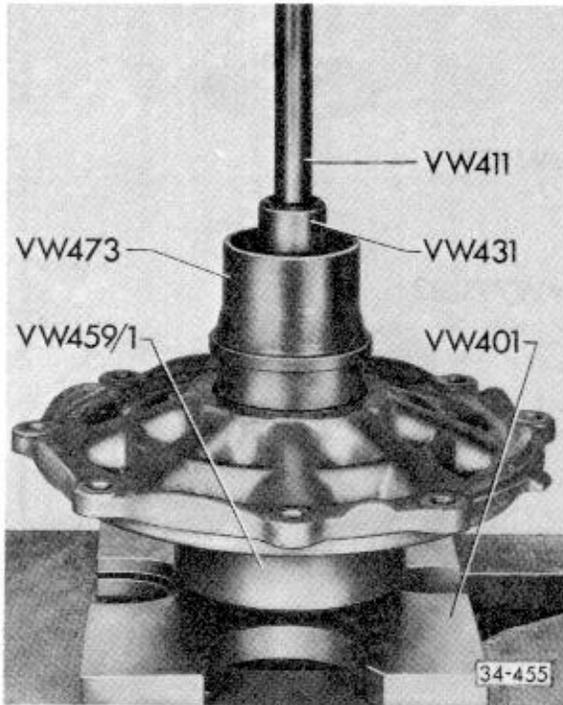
Außenring/Kegelrollenlager für Ausgleichgetriebe auspressen
